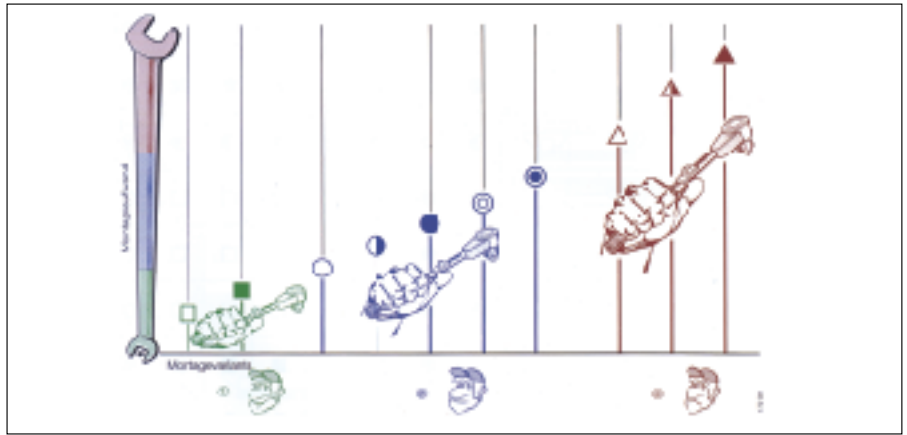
Linearführungen [3] – Montageaufwand nach Montagevariante beurteilen
